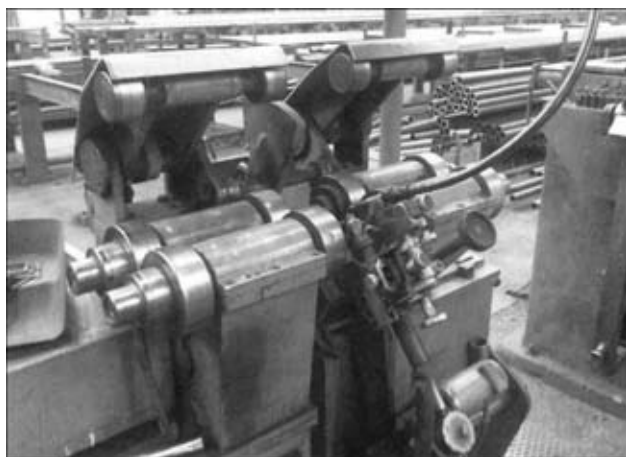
Трубосварочная установка типа VKW со сварочной головкой, установленной под стыком труб (с верхней подачей присадочной проволоки)
